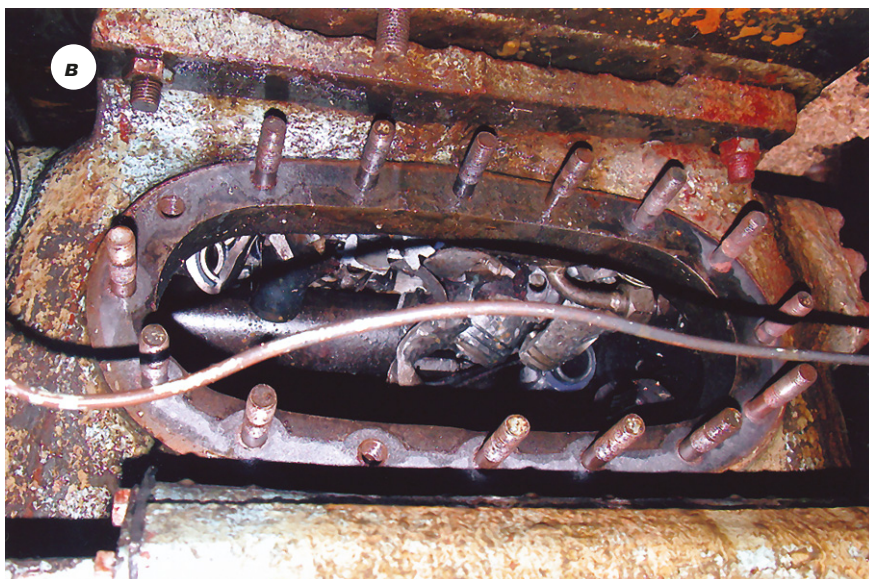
, а–в. Место аварии в ОАО «Хакасский молочный завод»: а – здание компрессорного цеха; б – деформация коленчатого вала компрессора; в – беспорядочное расположение деталей в картере компрессора после аварии
